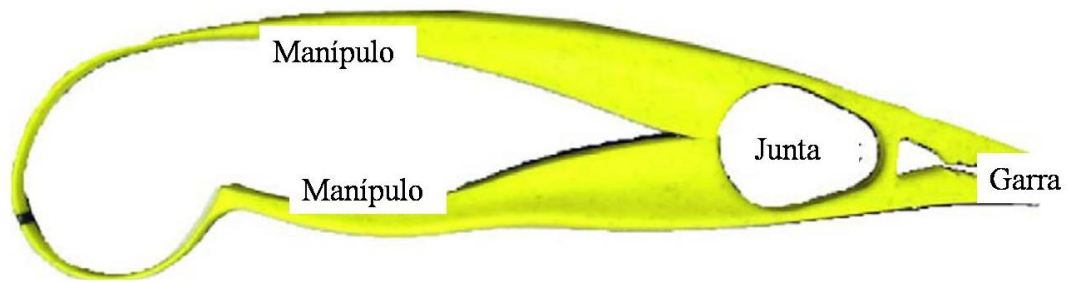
ALICATE EM MOLDE ÚNICO
